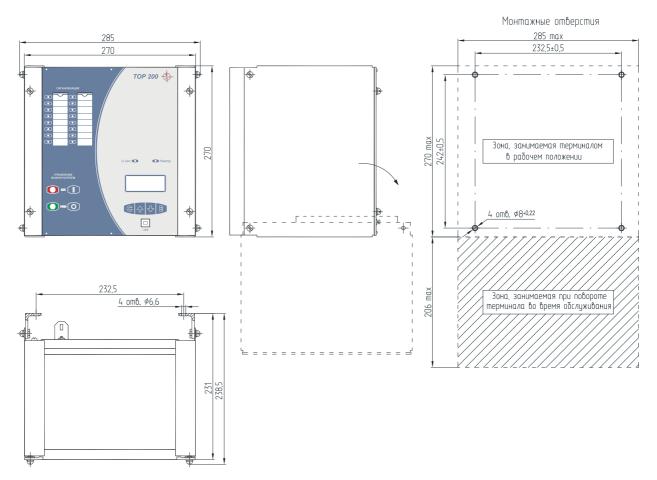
Габаритные и установочные размеры для навесного монтажа
